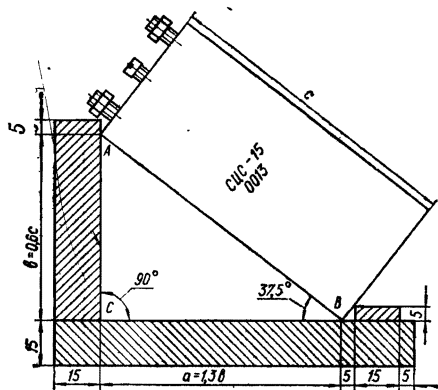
Эскиз приспособления для установки на пропитку серебряно-цинковых аккумуляторов.
